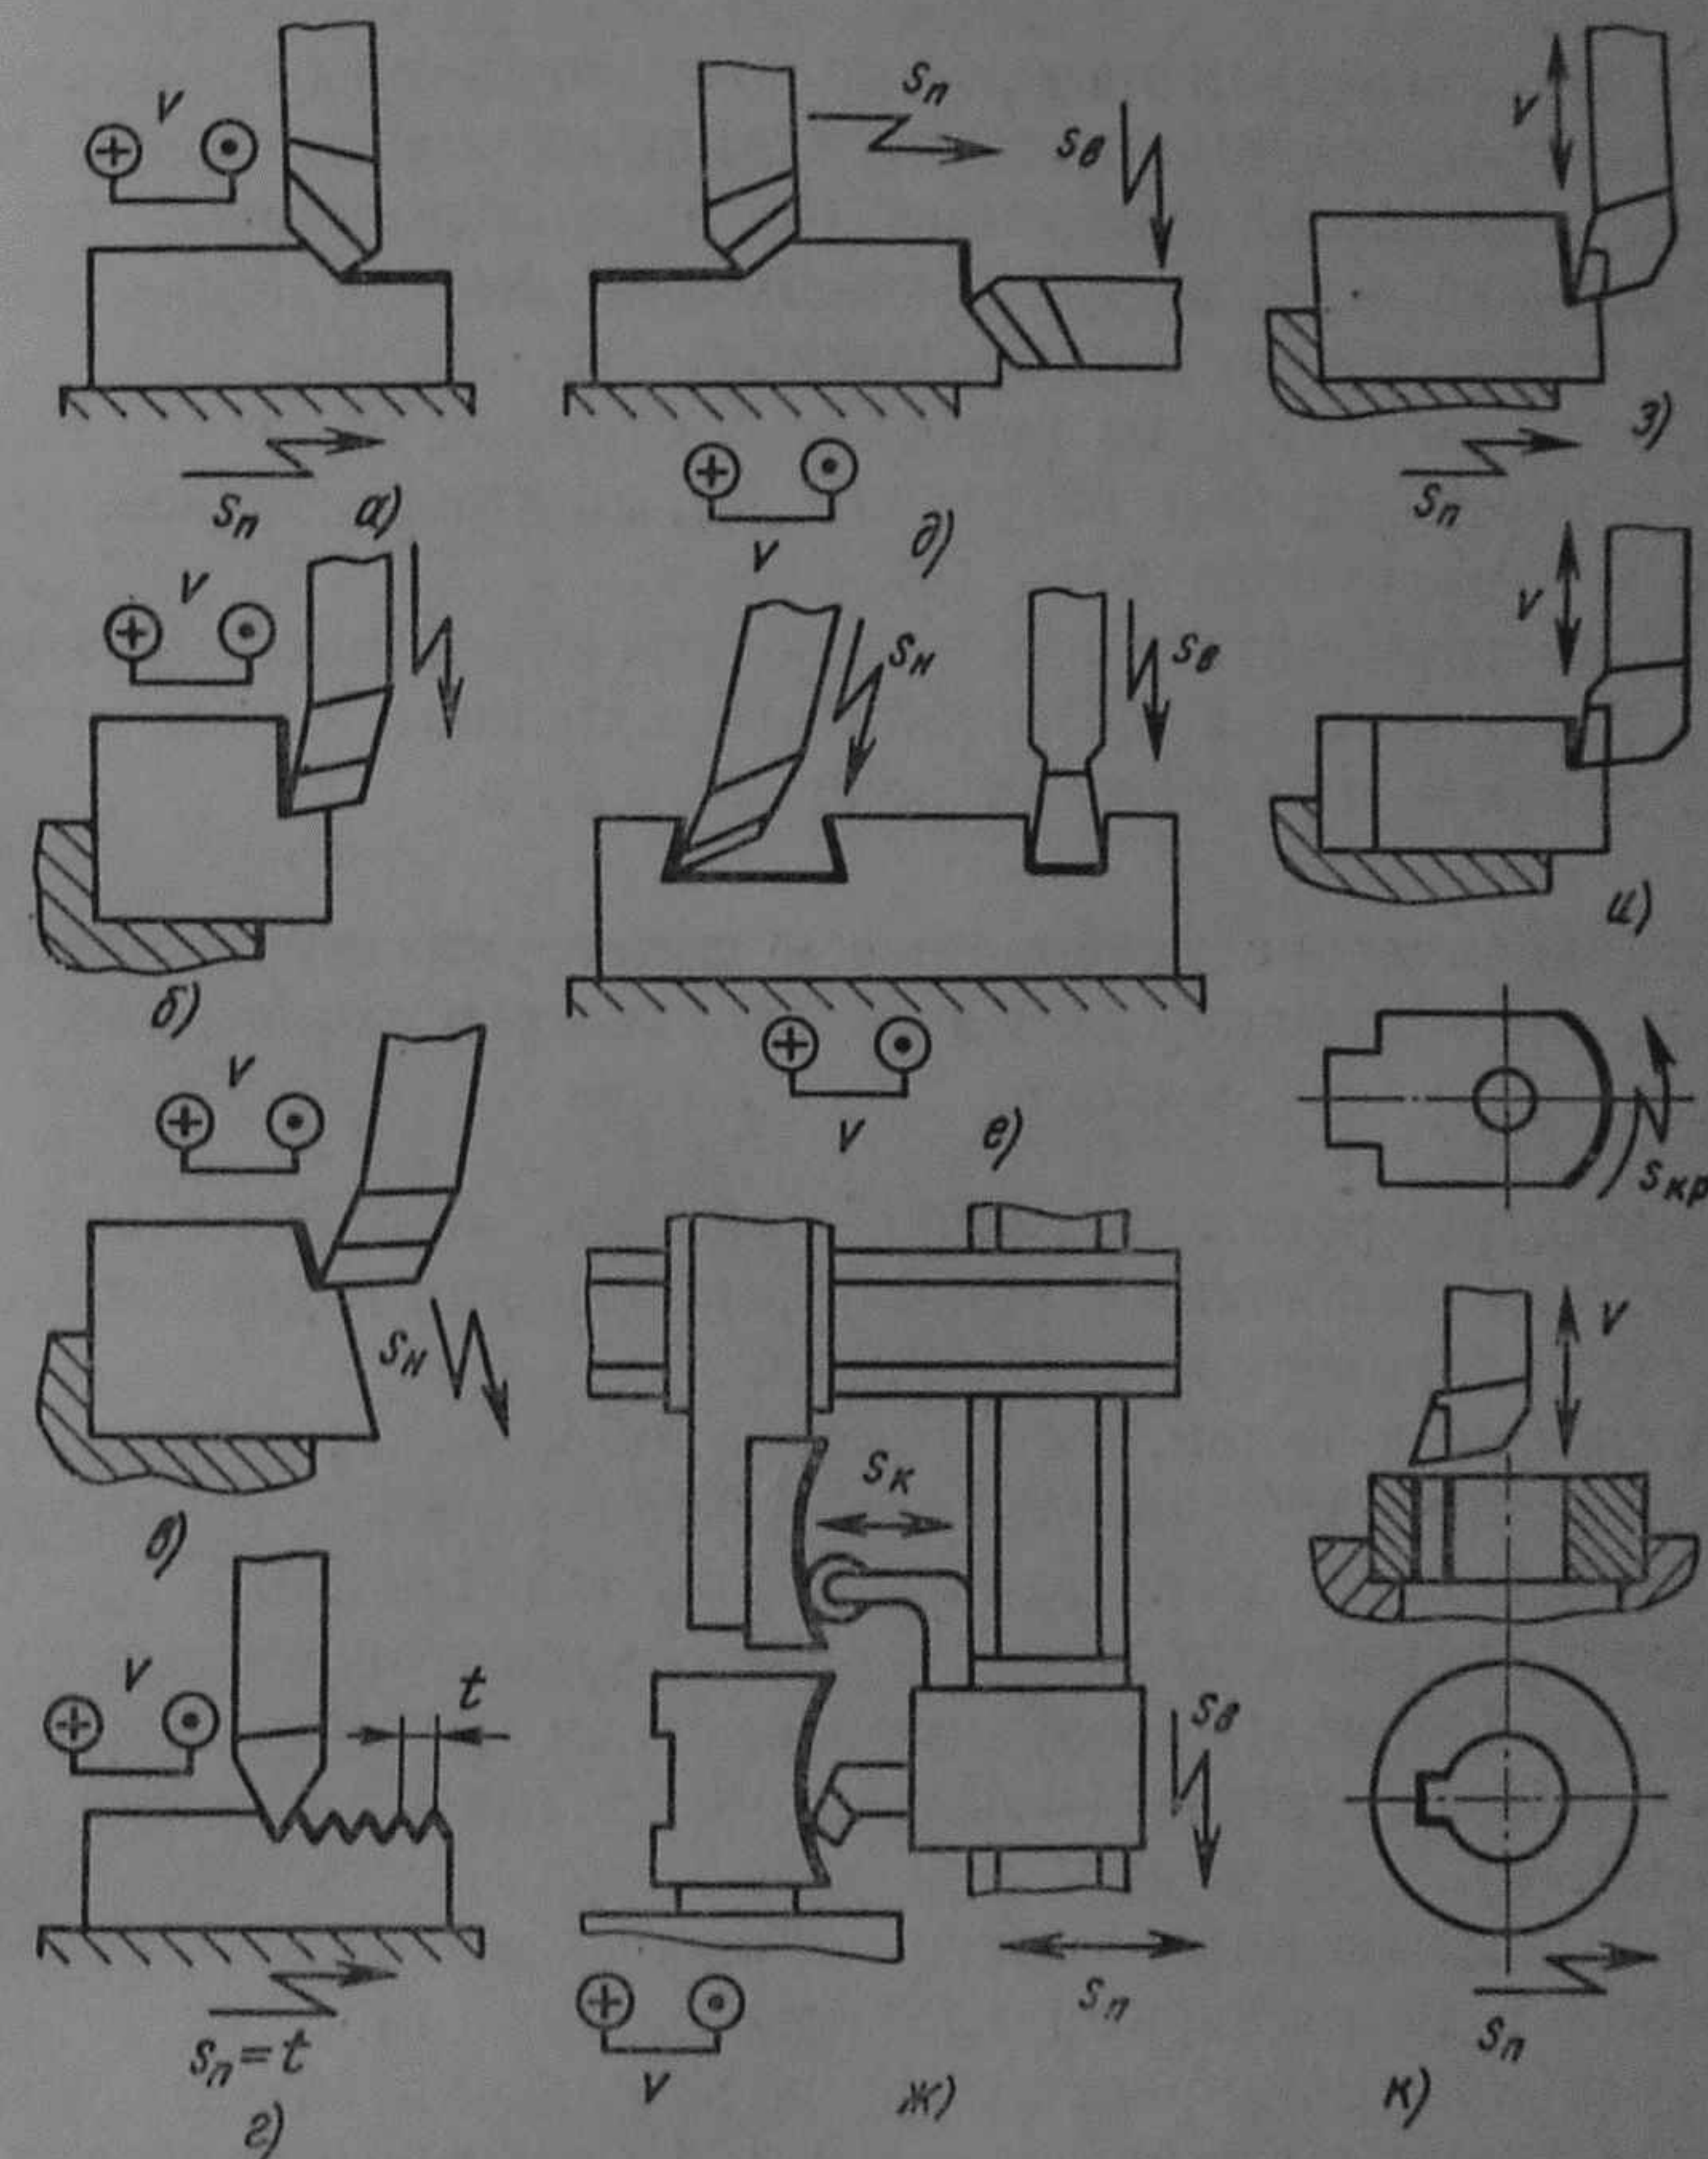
Схемы обработки поверхностей заготовок на строгальных и долбежных станках
